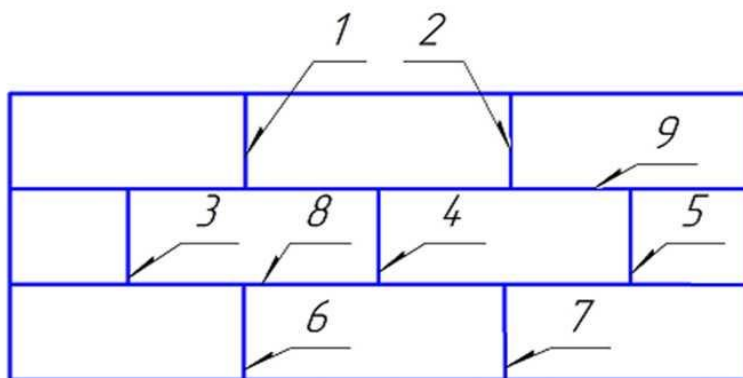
Последовательность сварки швов полотнищ
